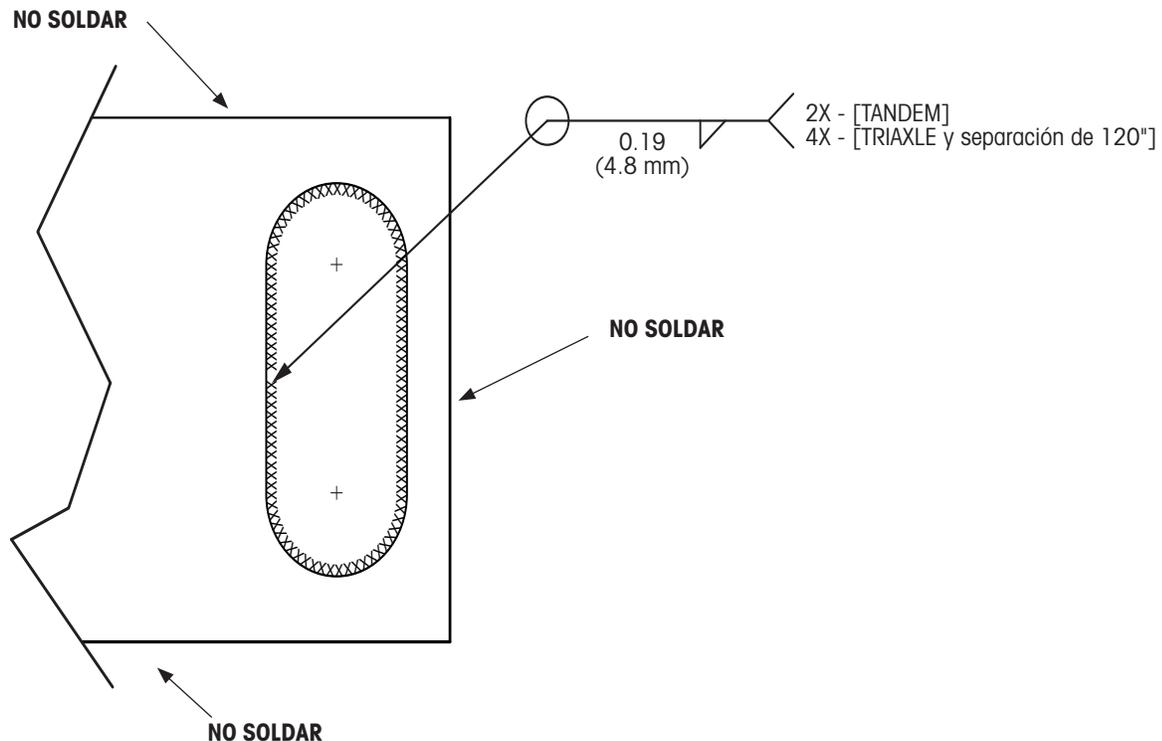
Soldadura de ventana del soporte del tanque
